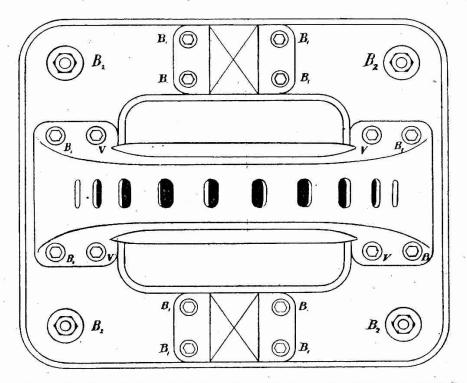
Fixation de la carcasse et des paliers sur la plaque de fondation.
